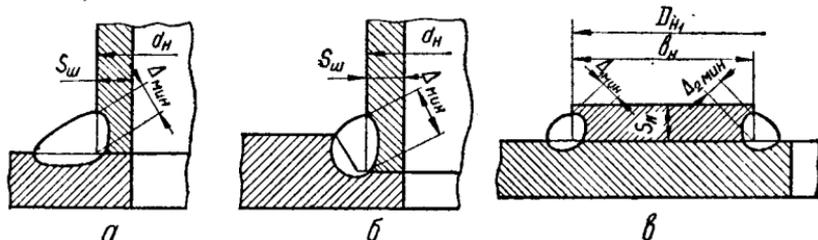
Размеры сварных швов укрепляющих элементов, применяемые при расчете:
